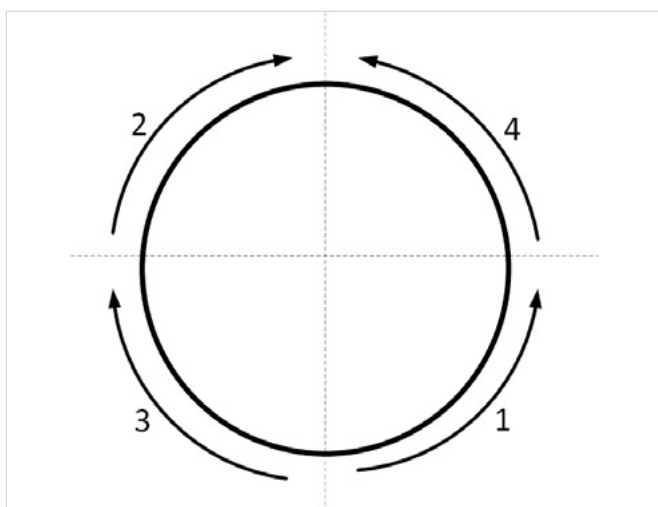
Расположение и очередность сварки участков корневого слоя шва: 1, 2, 3, 4 — последовательность сварки участков шва
